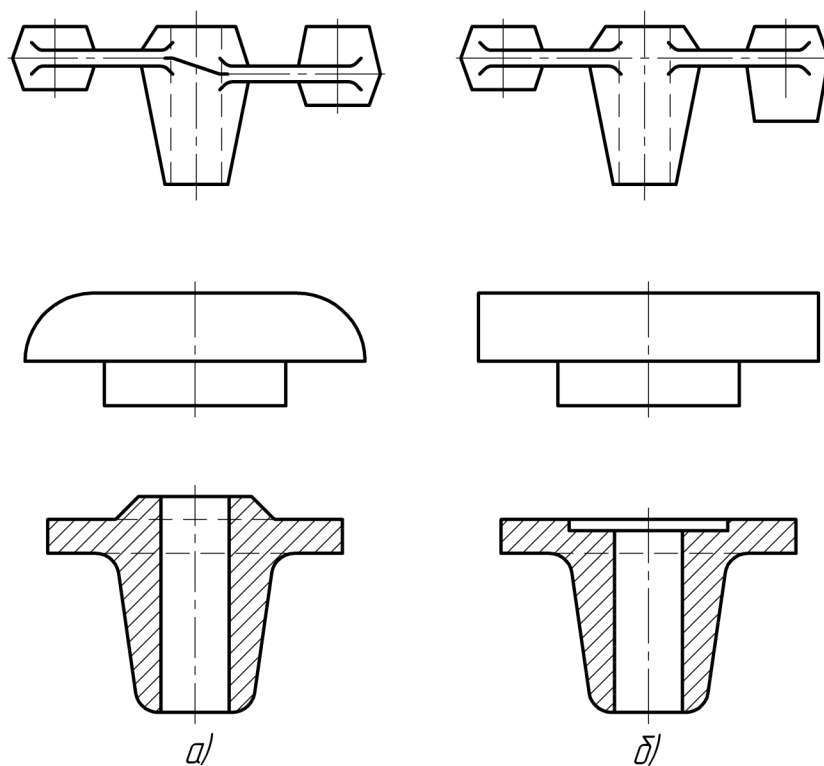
Примеры конструкций отливок (сборные конструкции)
